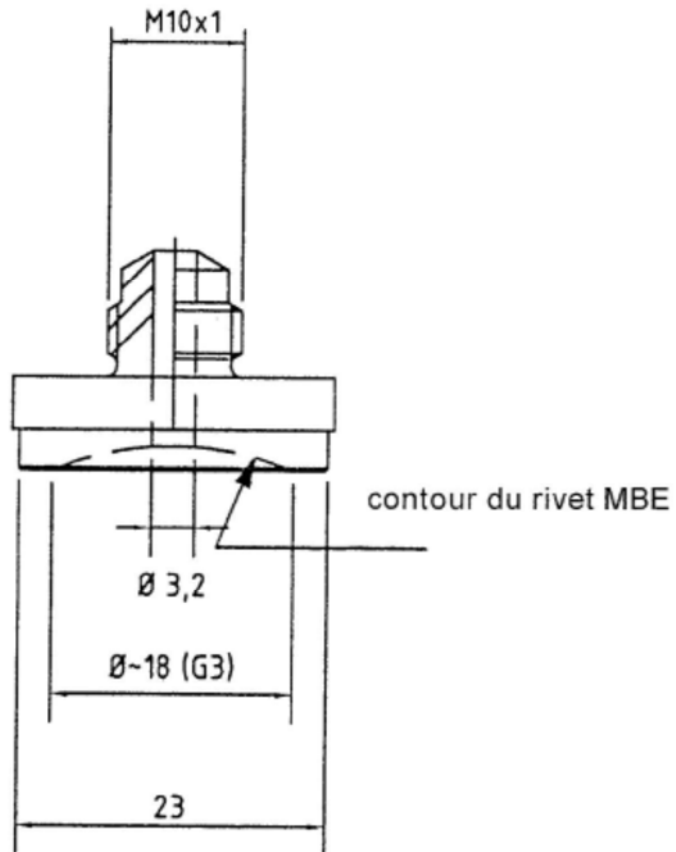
bis – Cale de serrage pour fixation des points coulissants
